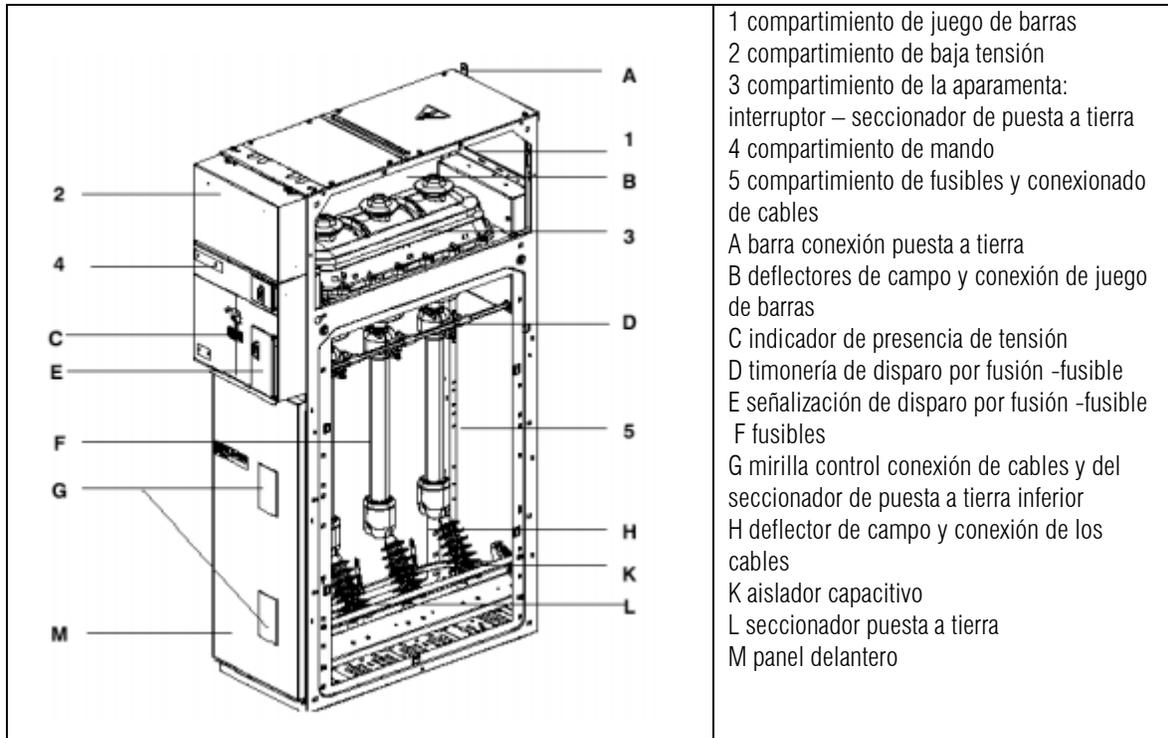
Accesorios de seccionador-fusible en SF6.
